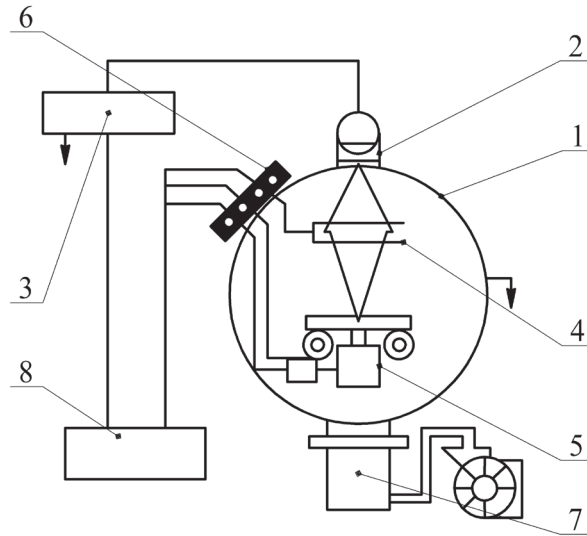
Схема установки для сварки электронным лучом:
